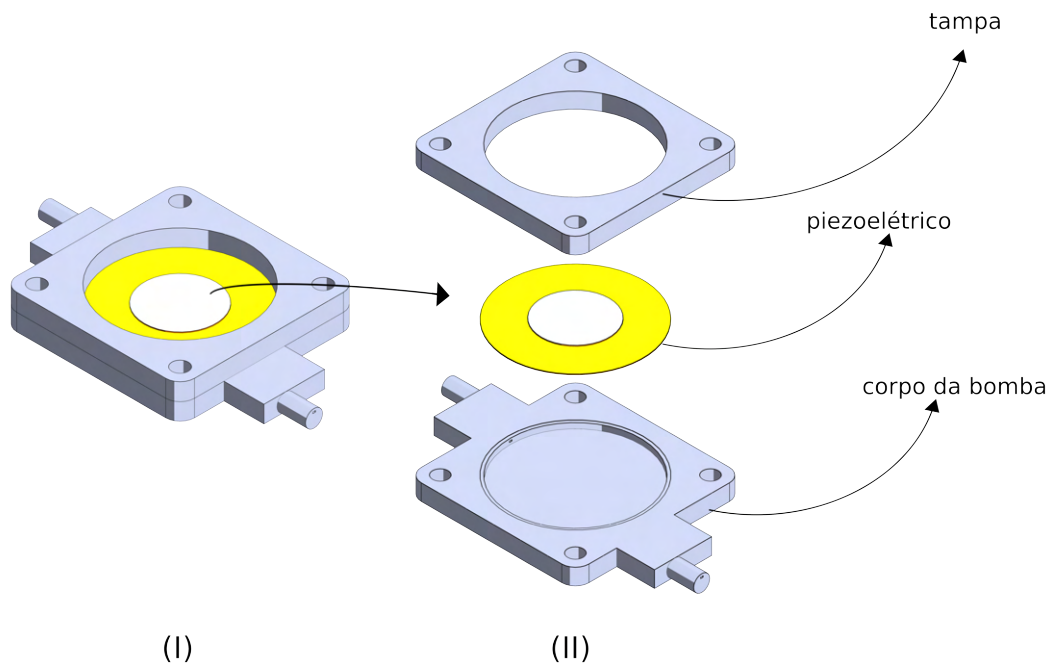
(I) Bomba montada e (II) seus componentes.
